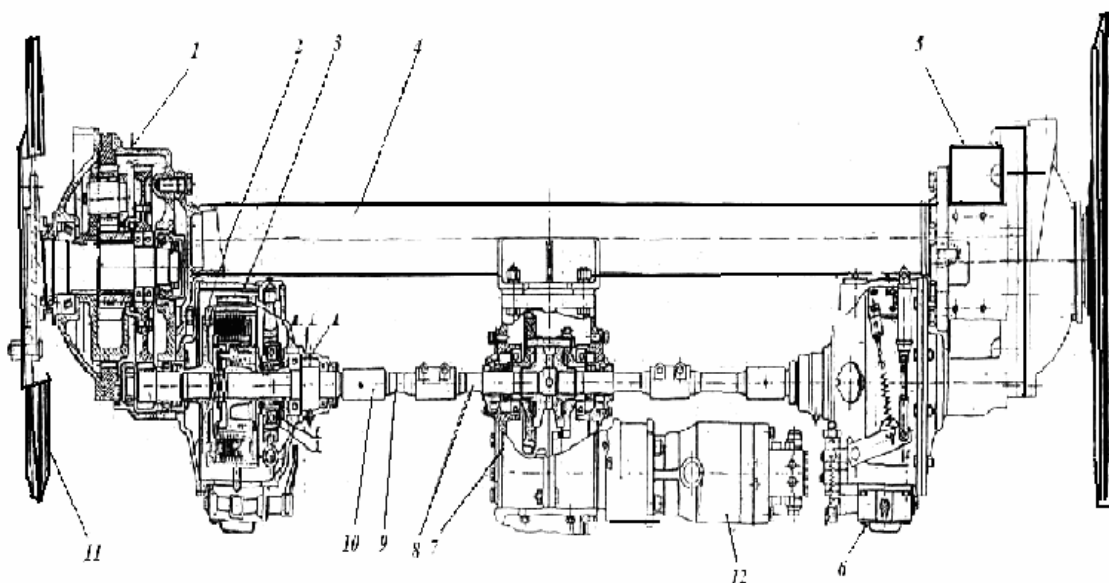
Мост ведущий 1 – редуктор бортовой правый; 2 – барабан со ступицей; 3 – фрикцион бортовой правый; 4 – балка моста ведущего; 5 – редуктор бортовой левой; 6 – фрикцион бортовой левой; 7 – коробка диапазонов; 8 – полуось правая; 9 – полуось; 10 – втулка соединительная; 11 – звездочка ведущая; 12 – гидромотор
